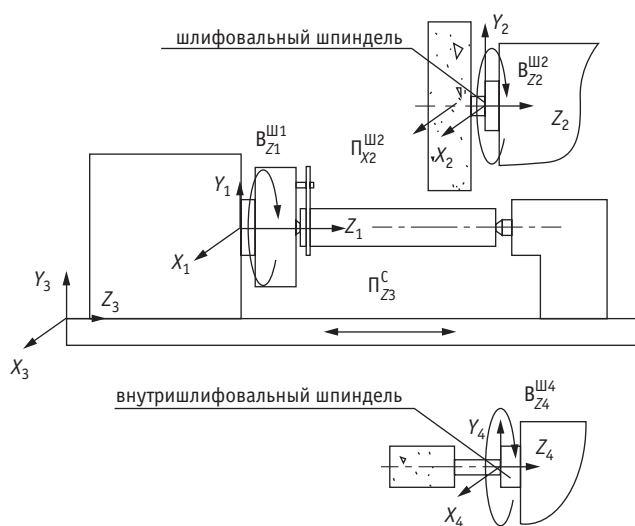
Формообразующие движения рабочих органов станка ОШ-510Ф2
